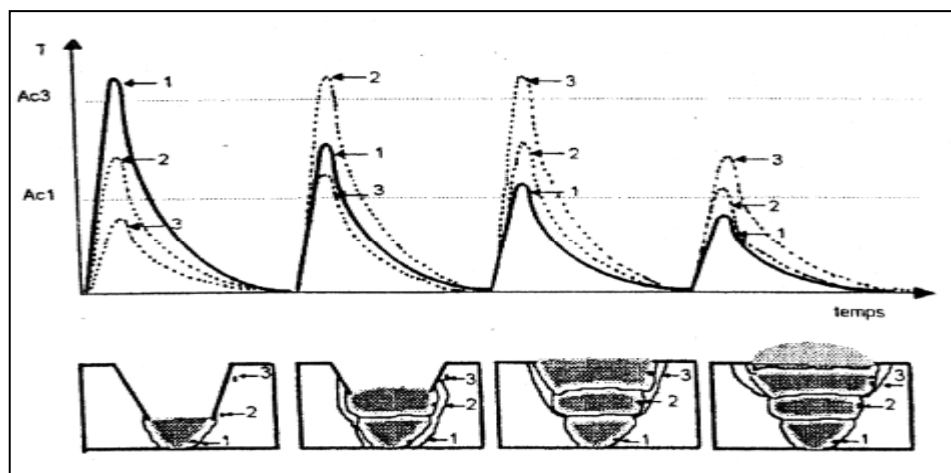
Cycle thermique pour le soudage multi passes.
